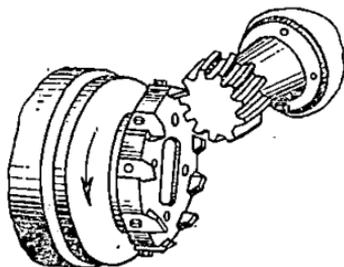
Обработка конического зубчатого колеса торцовой зуборезной головкой.
